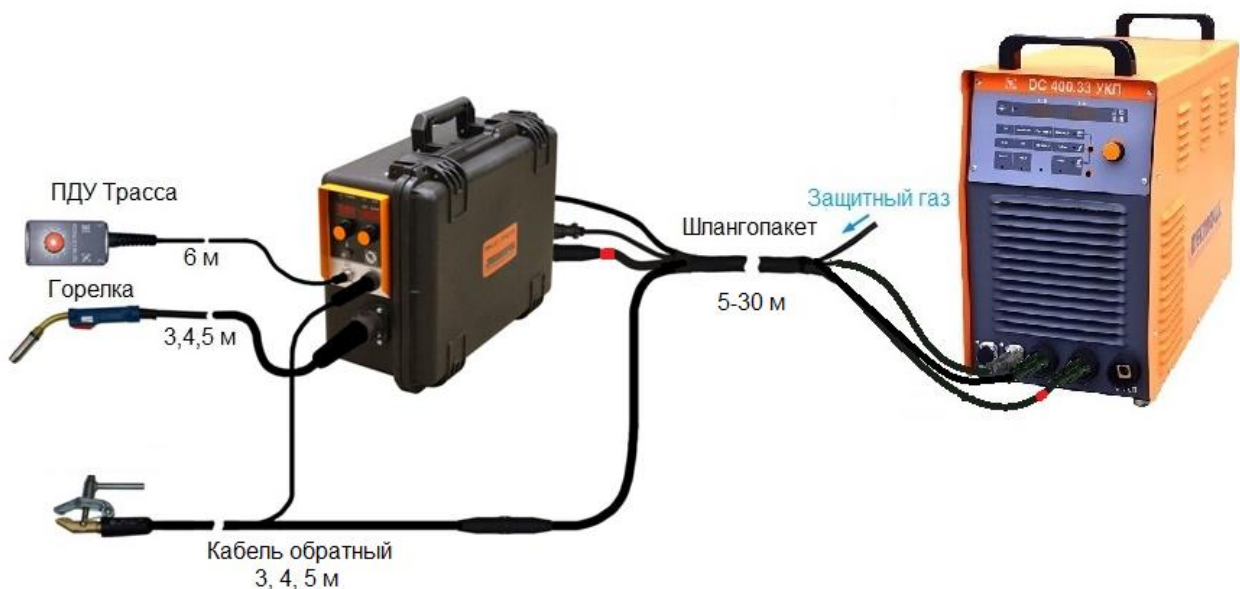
Схема сборки при сварке в режиме ПА
